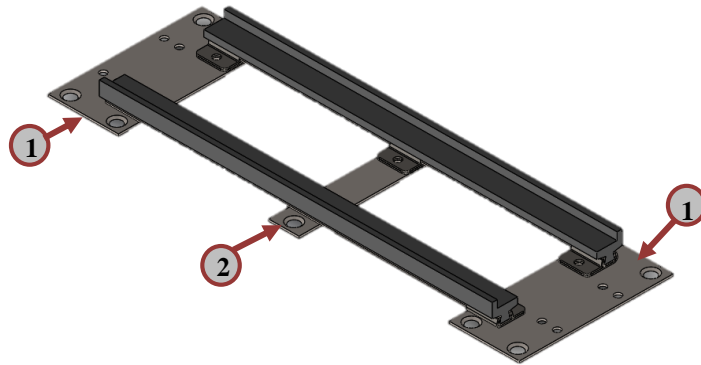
Dibujo CAD que muestra las placas de soporte para fijar elementos de superficie de apoyo de la banda transportadora.
